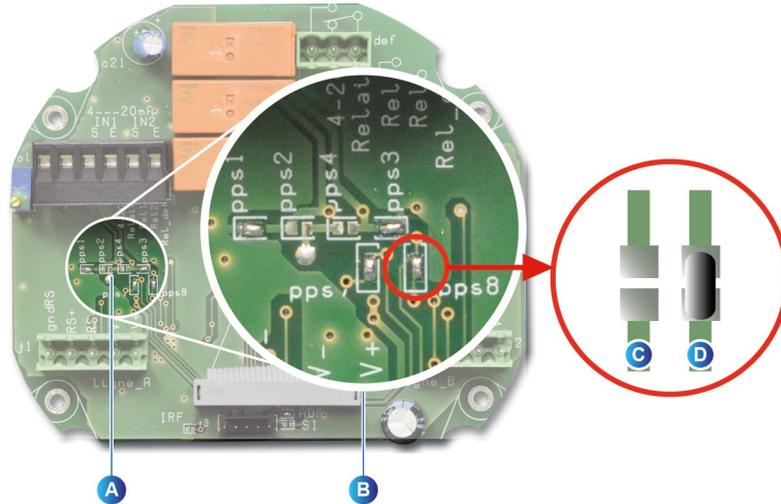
ejemplo de una almohadilla de soldadura con y sin una unión de soldadura.
